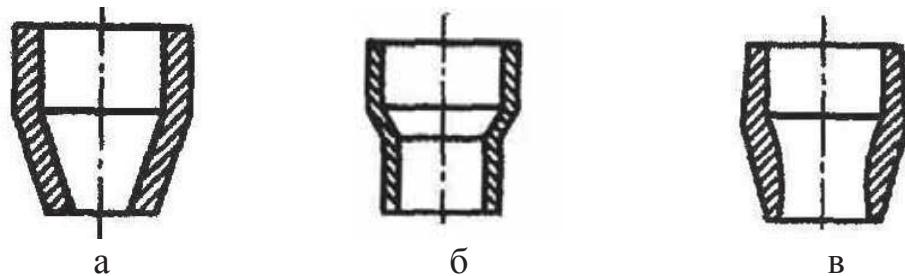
Формы сопел сварочных горелок: а – коническая; б – цилиндрическая; в – профилированная
